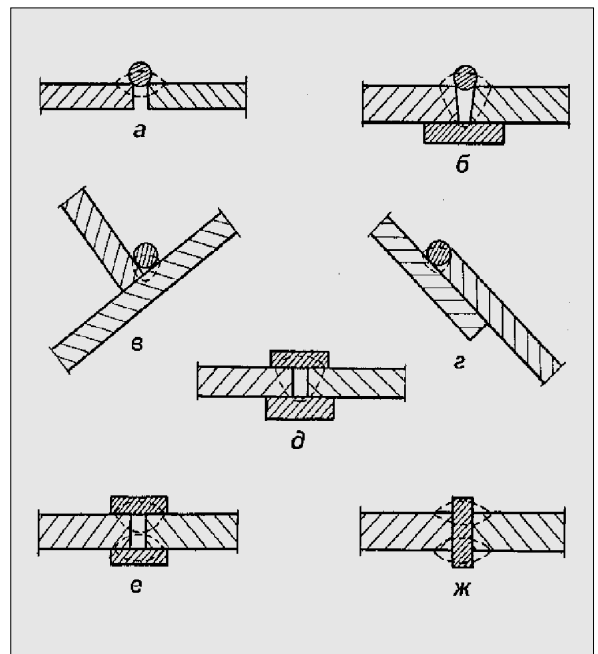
Сварные соединения с укладкой присадочного материала
